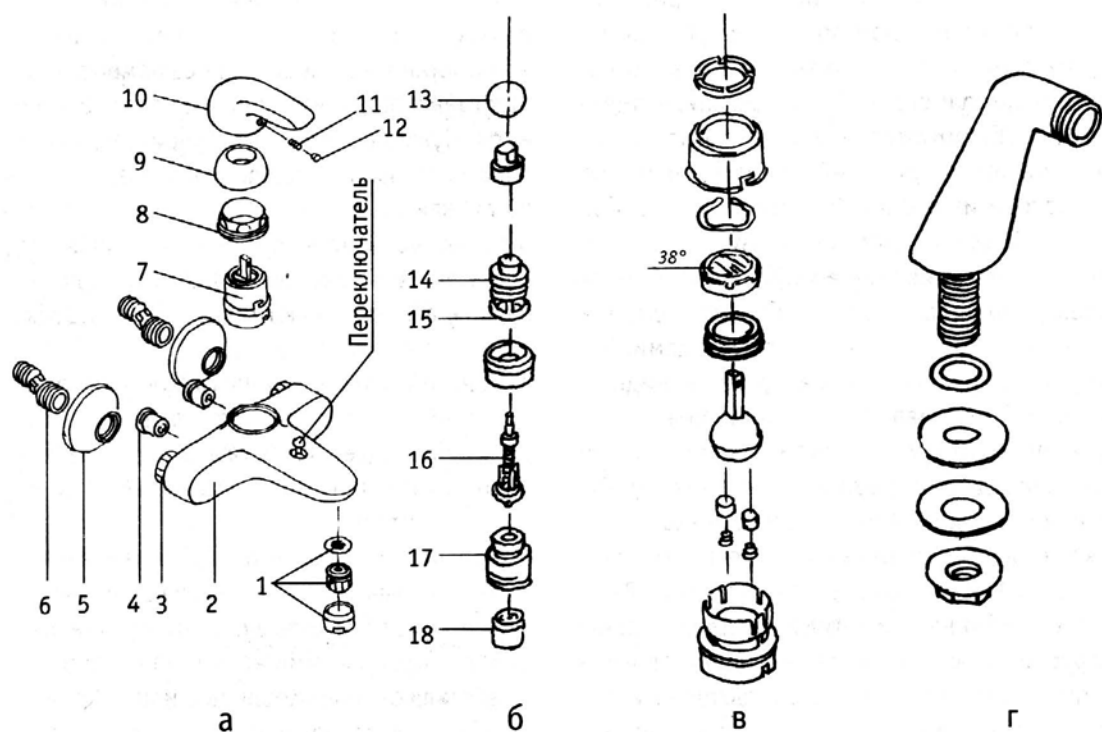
Однорычажный смеситель с золотниковым переключателем «ванна—душ» фирмы «Ханс-гроз»: а — деталировка смесителя, б — деталировка переключателя, в — деталировка картриджа, г — переходник
